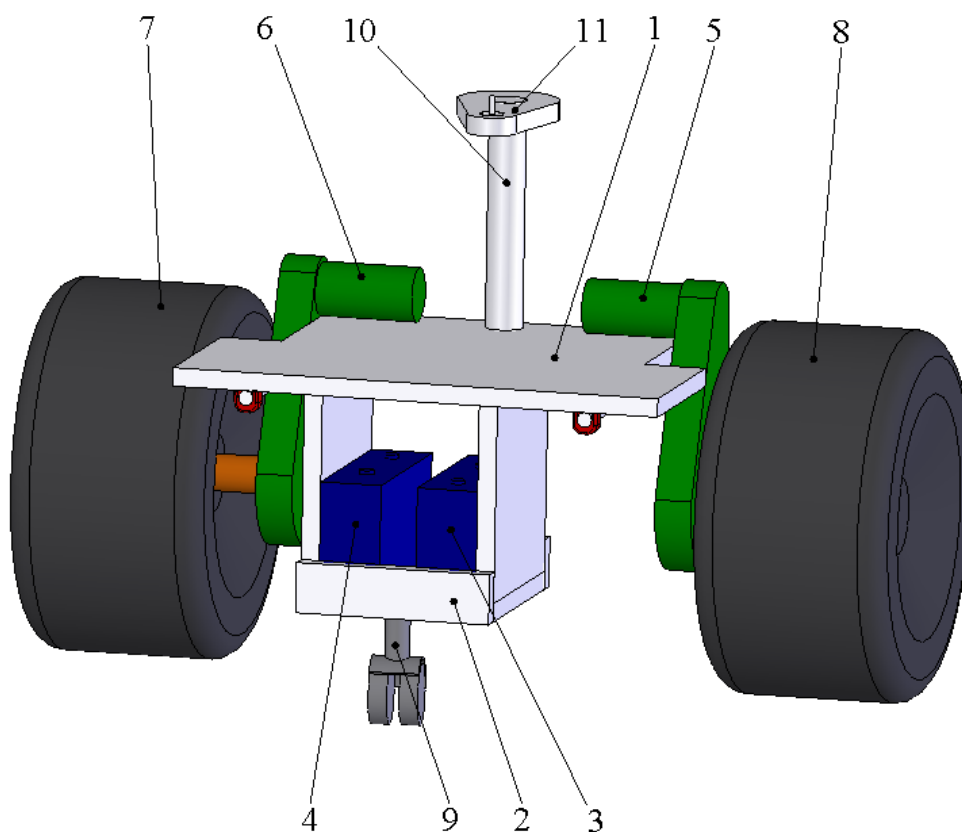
Общий вид платформы: 1 – основание; 2 – аккумуляторный короб; 3,4 – аккумуляторы; 5,6 – мотор-редукторы; 7,8 – ведущие колеса; 9 – поворотное колесо; 10 – опора локатора, 11 – площадка.
